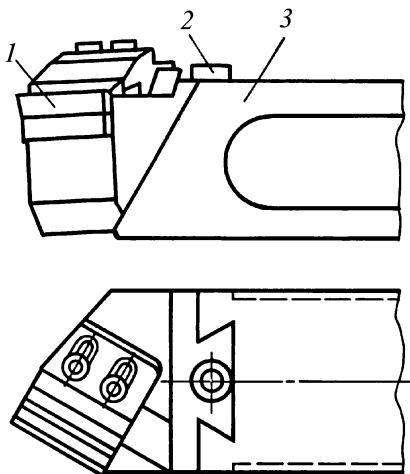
Сборный резец со сменными резцовыми вставками
